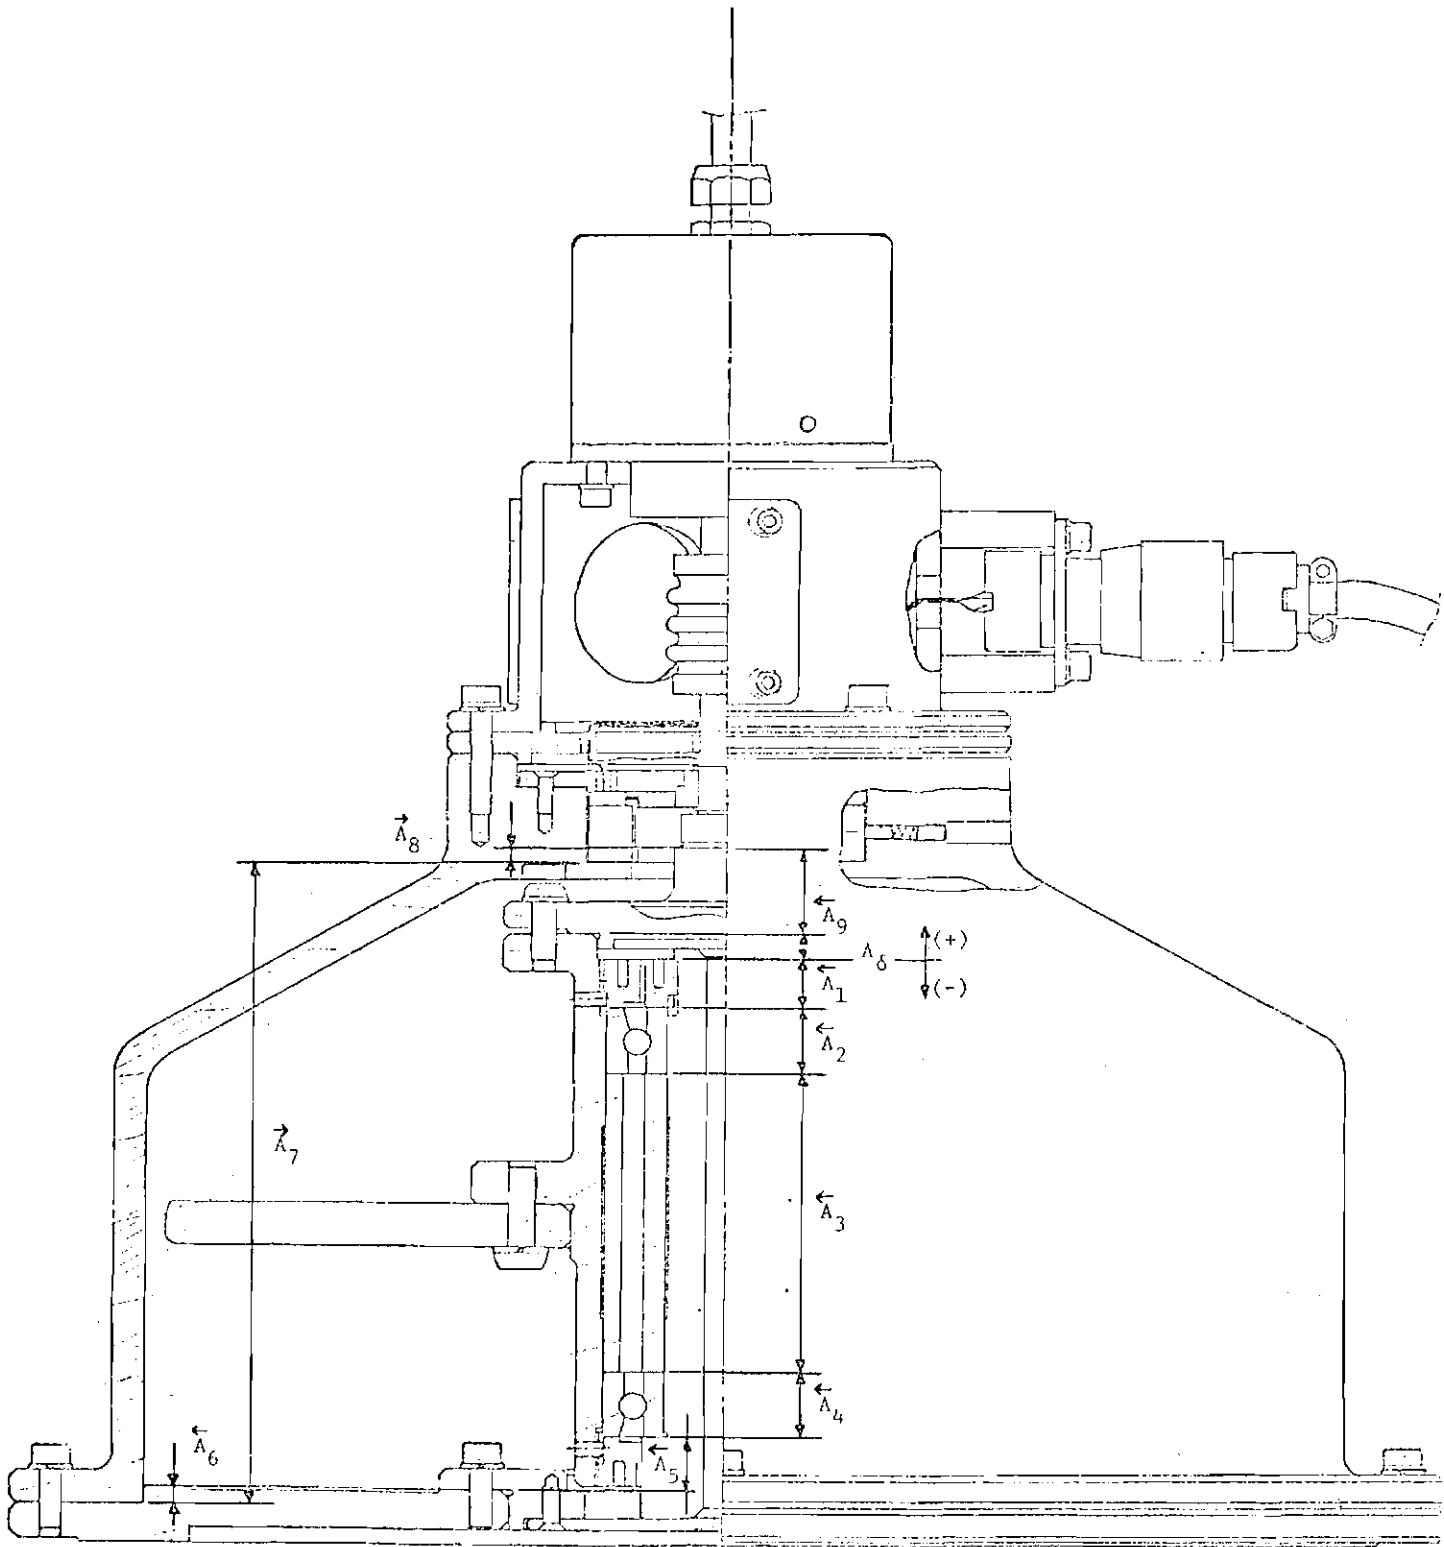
Roda de reação e sua cadeia de dimensões.
